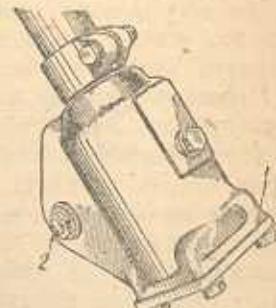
Регулировка осевого люфта вала рулевой сошки:
